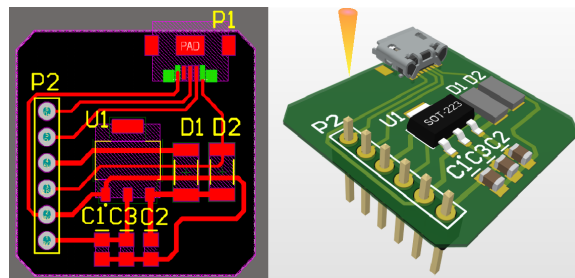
Diseño PCB para conexión USB y regulador de voltaje.
